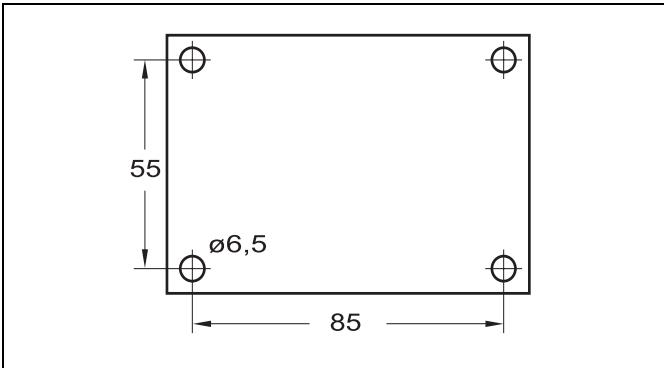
Lochbild für Ständer Umwälzpumpe U 4856
